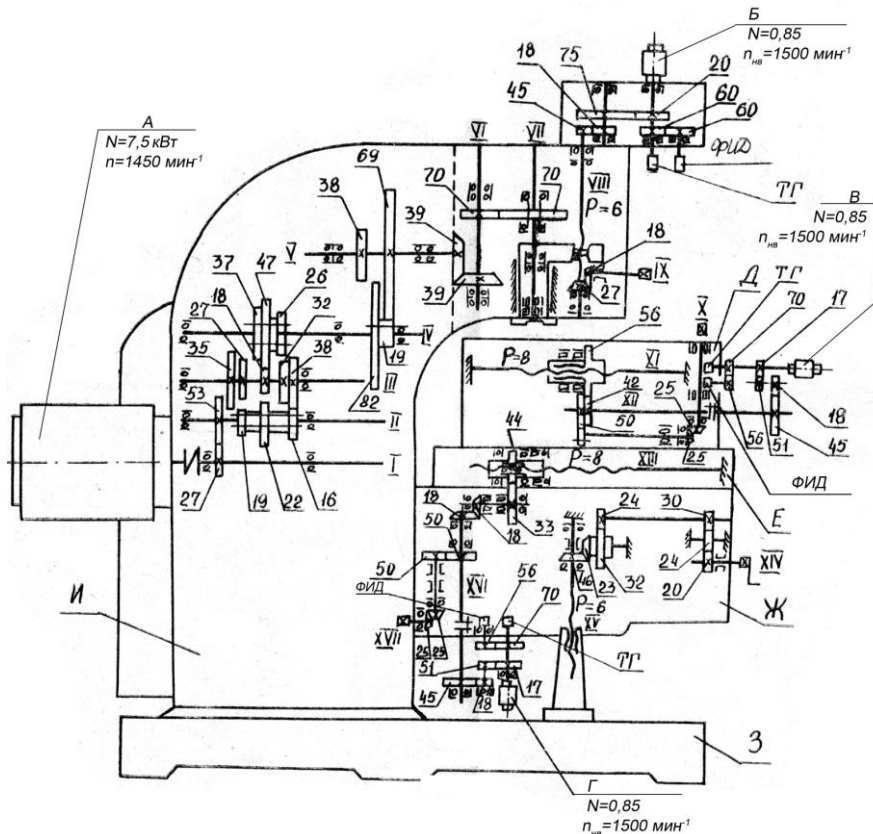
Кинематическая схема и основные узлы станка 6М13ГН1:
